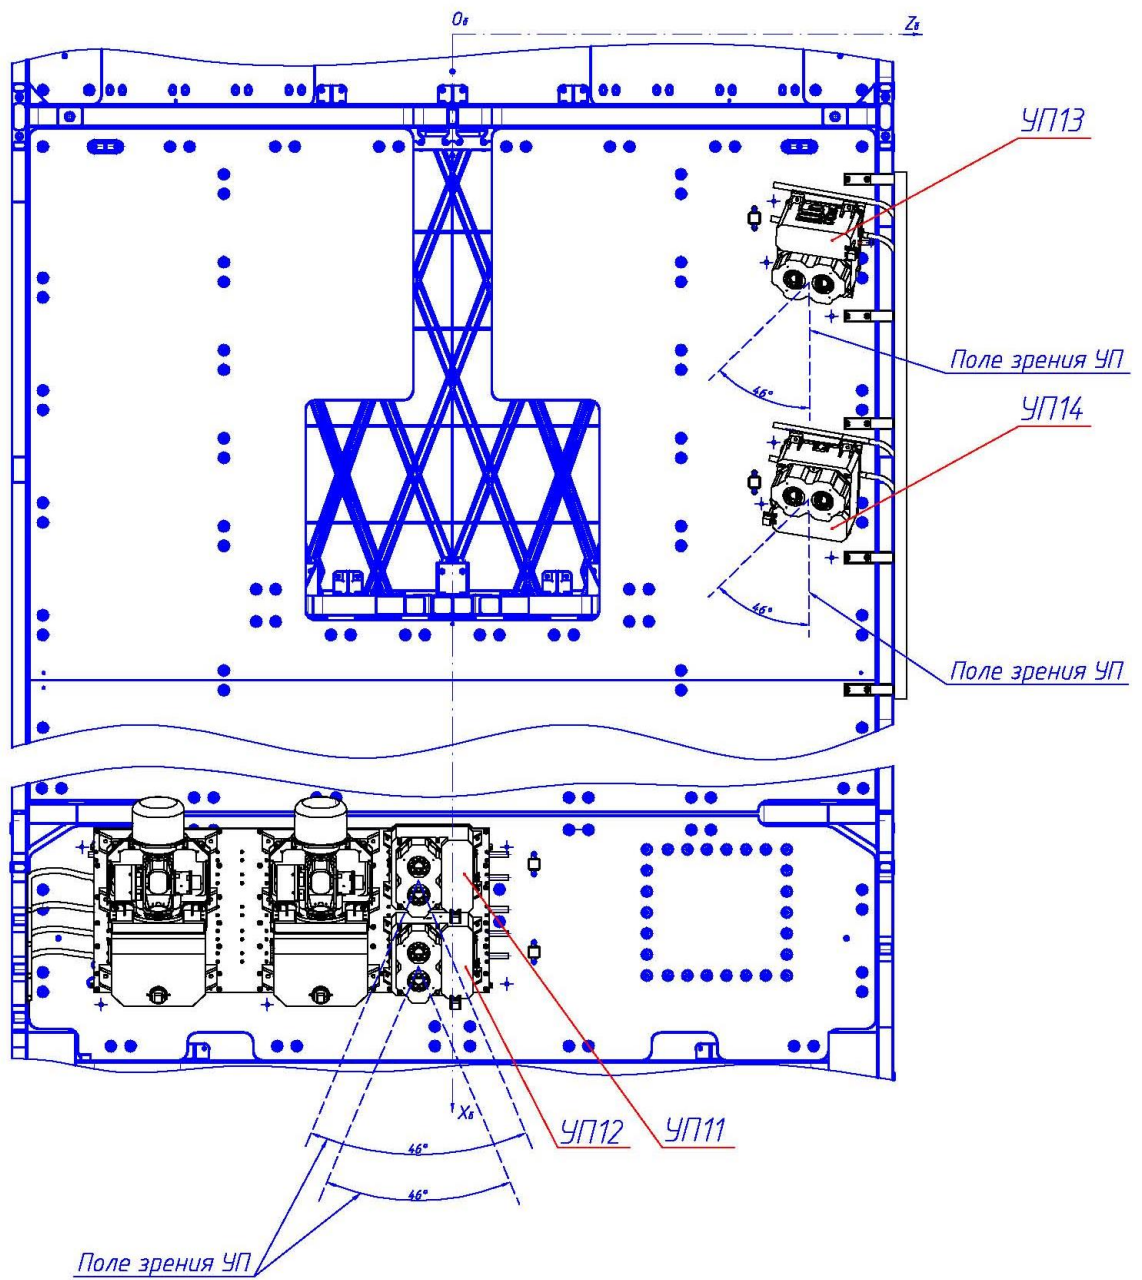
Размещение УП на корпусе КА (Вид Б)
